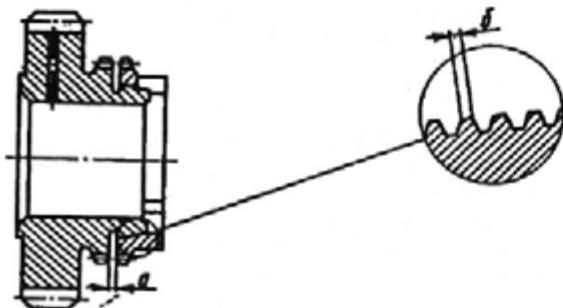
Установка блокирующего кольца синхронизатора на кус шестерни
